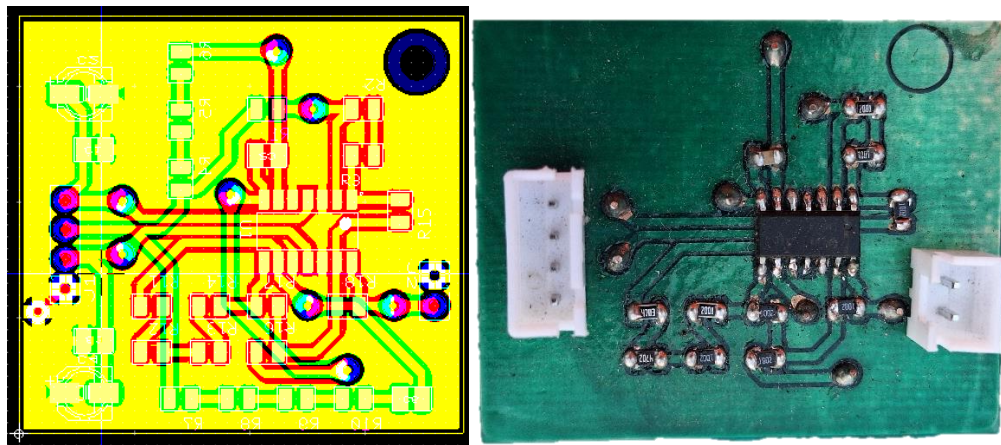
Diseño y manufacturación del PCB para el controlador proporcional-integral-derivativo
